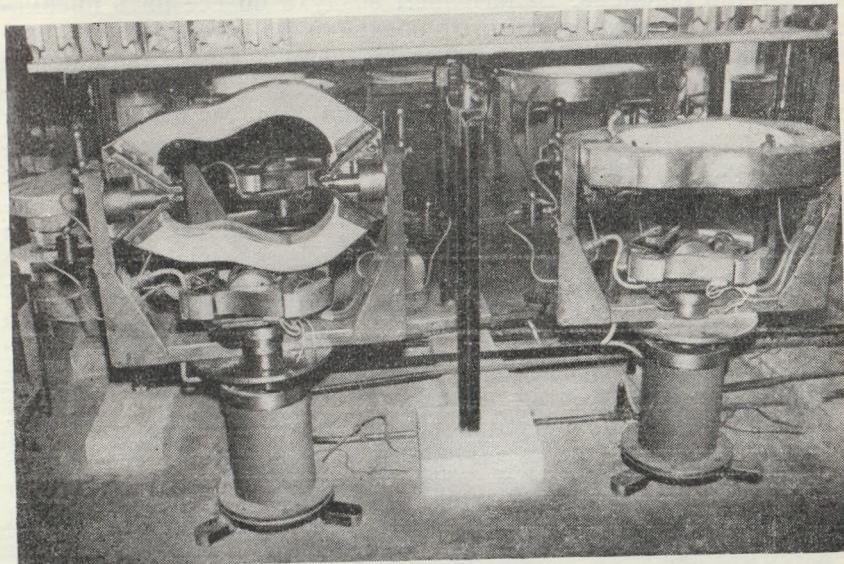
Пневматические ваймы с электрическим контактным нагревом для сборки рамки корпуса гитары
